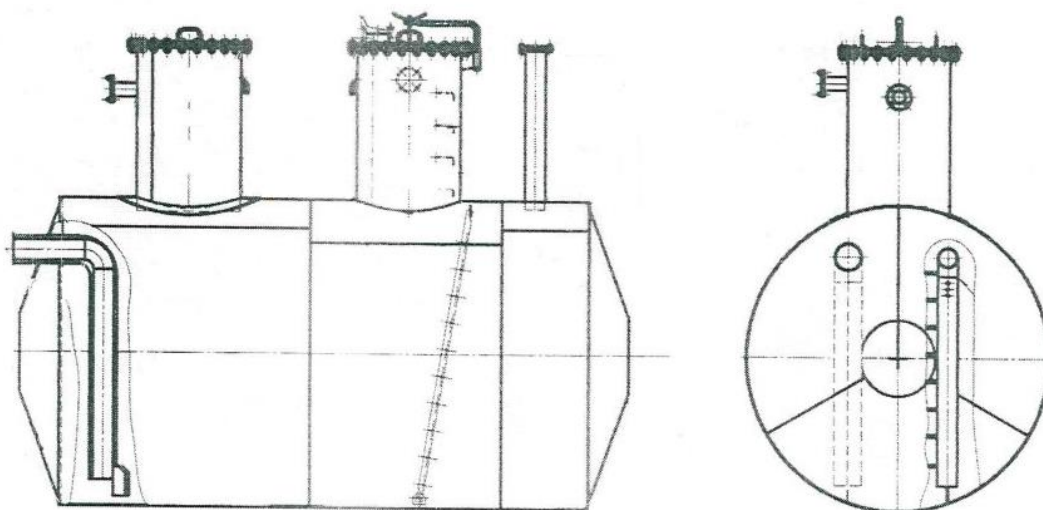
Общий вид эскиза резервуара ЕП-20
